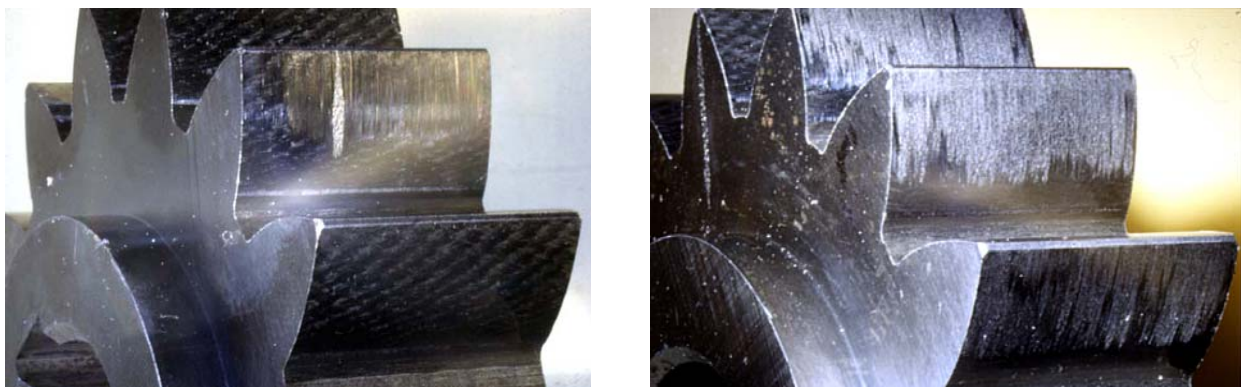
Riefen mit einem Fressstrich (links) und Fresser über der gesamten Flanke (rechts) an Ritzeln der FZG-Testverzahnung Typ A20
